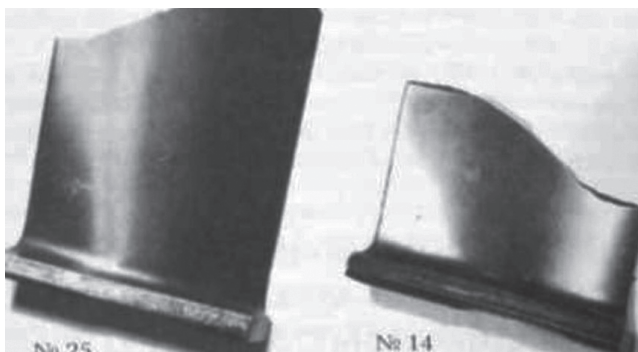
Поломка лопаток 1-й ступени компрессора высокого давления двигателя Д-30КУ [6]
